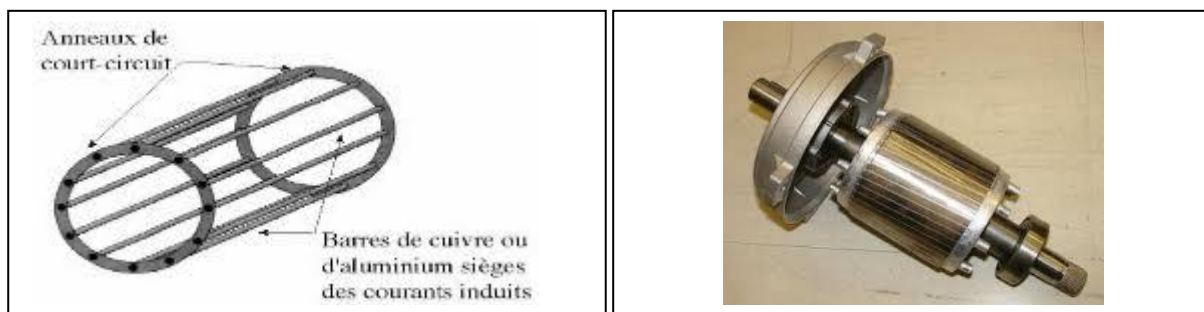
Dessin structurel de rotor à cage [12]. Figure I.6 Dessin réel de rotor à cage [13].
